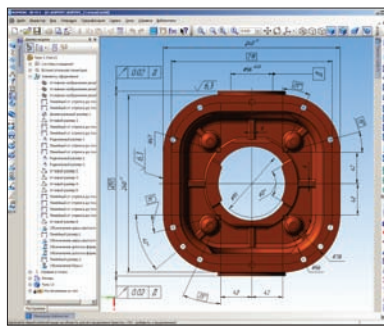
Корпус. Вид снизу с условными обозначениями в 3D
